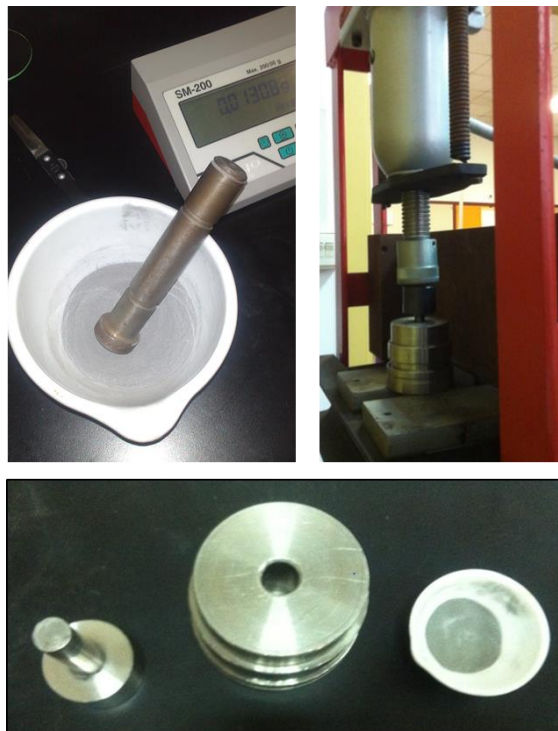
Mezcla en mortero y molde cilíndrico para prensado hidráulico.
